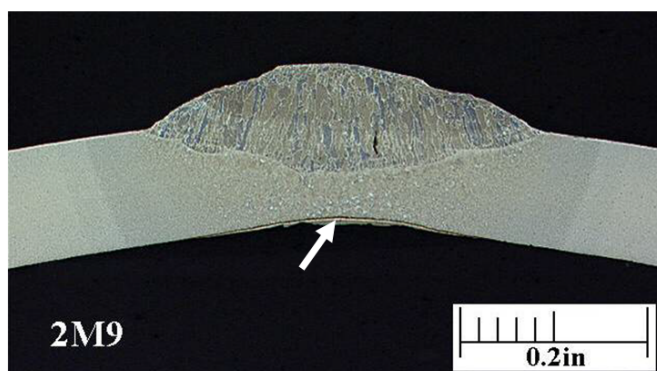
Макроструктура зварного з'єднання при наплавленні валика на поверхню труби [10]
